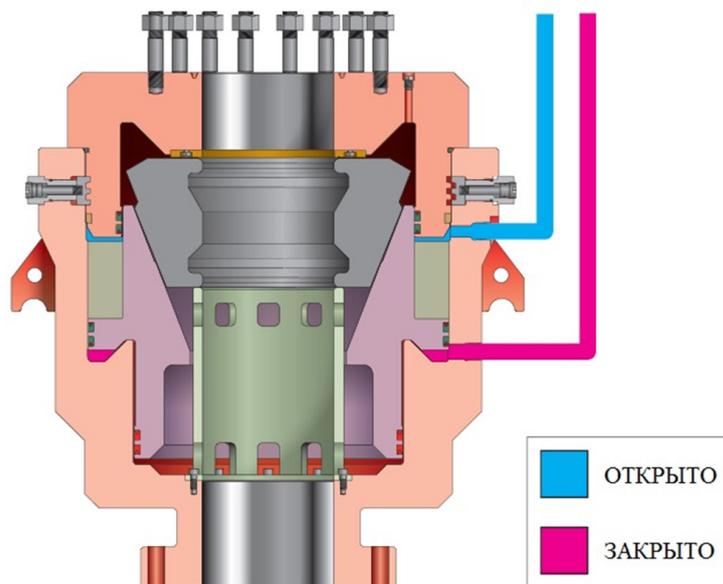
Превентор универсальный кольцевой ПУГ: 1-крышка; 2-уплотнитель кольцевой конический; 3-поршень, 4-предохранительная втулка; 5-корпус;
